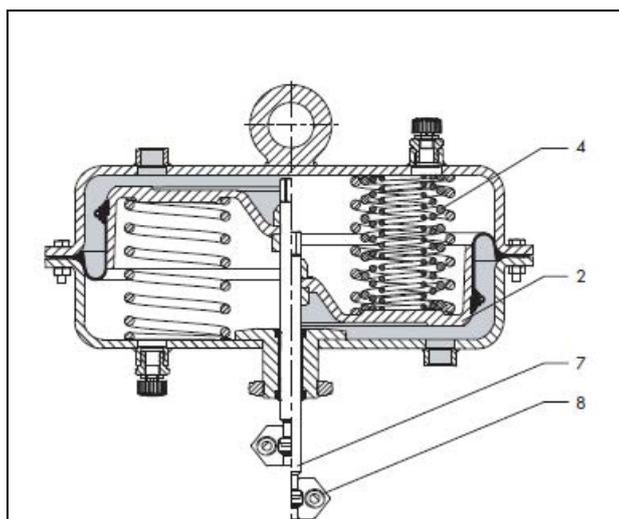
Пневматический привод Тип 3271, 1400-60 см², в сечении
